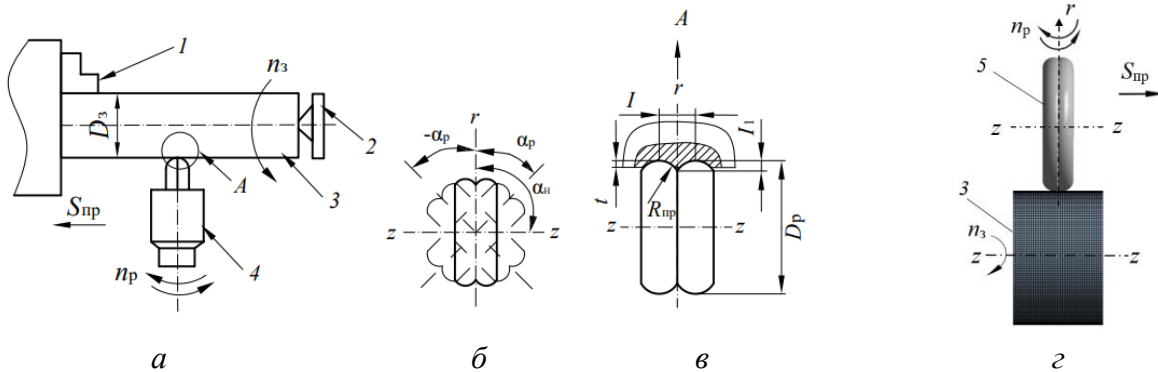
Схема реверсивного выглаживания двухрадиусным роликом (а), схема реверсивного вращения рабочего инструмента (б), рабочей зоны (в) и конечно-элементная модель процесса упрочнения (з): 1 – трехкулачковый патрон; 2 – задняя бабка; 3 – заготовка; 4 – рабочий инструмент; 5 – двухрадиусный ролик
